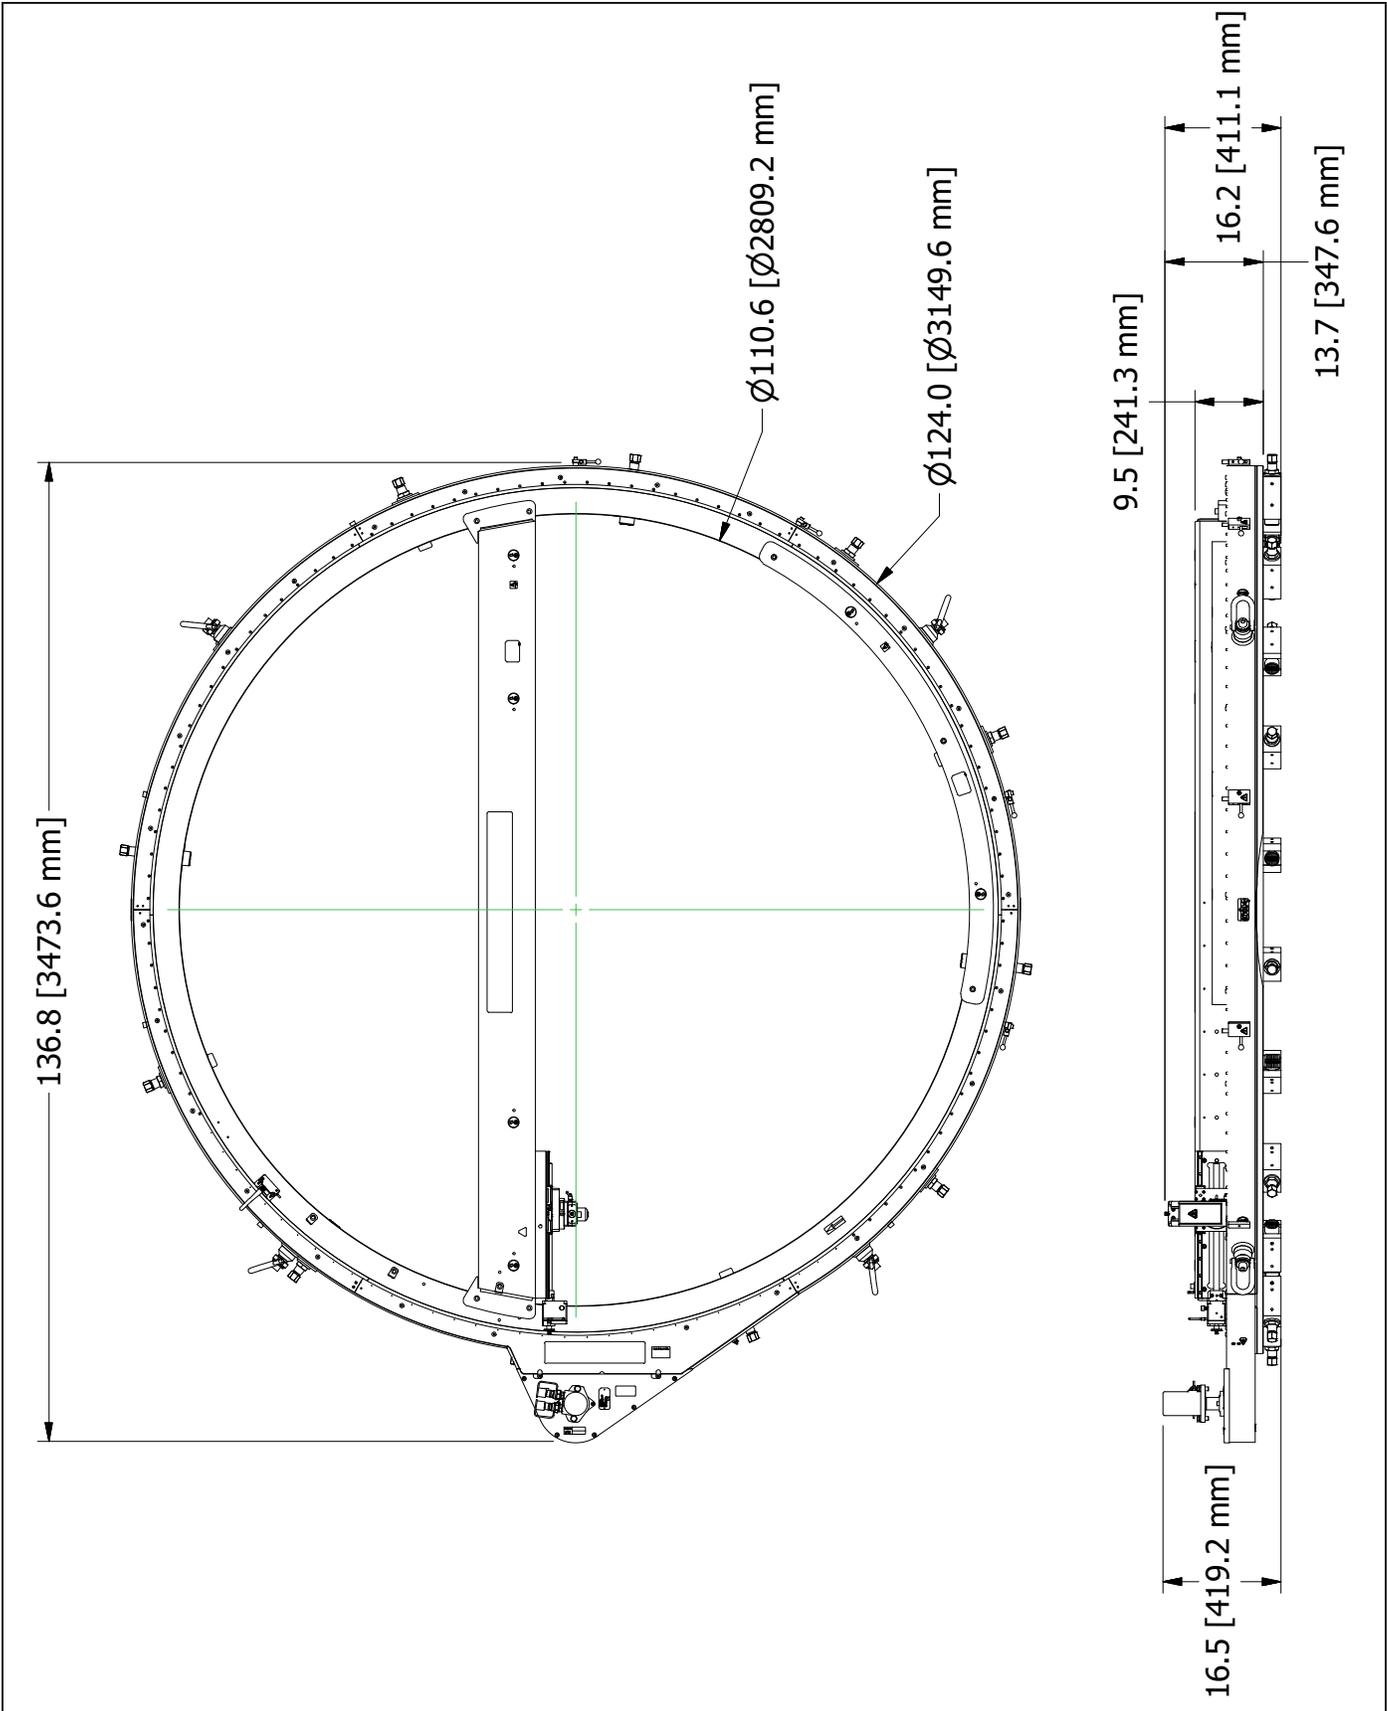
DIMENSIONS DE LA SURFACEUSE RAPIDE ODF110 SPEED FACER (REF. 93050)
